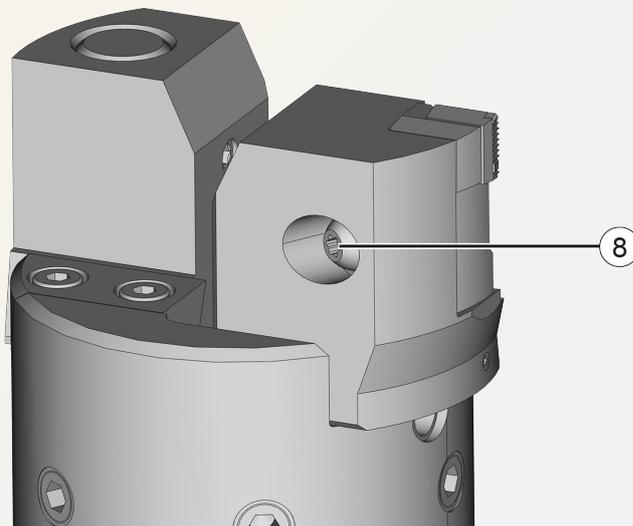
Serrage de la vis de serrage du porte-plaquette avec couple défini
